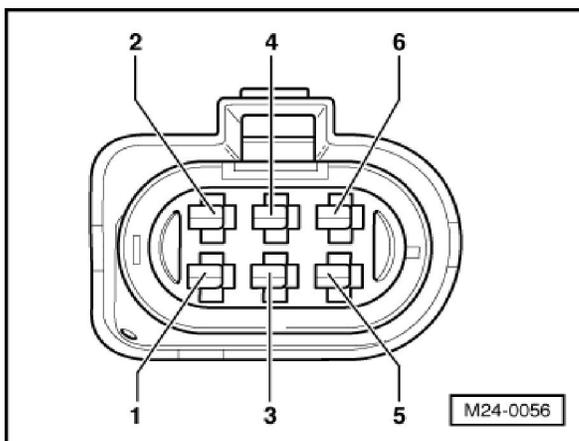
Conector de 6 contactos del lado hacia UCE motor.
